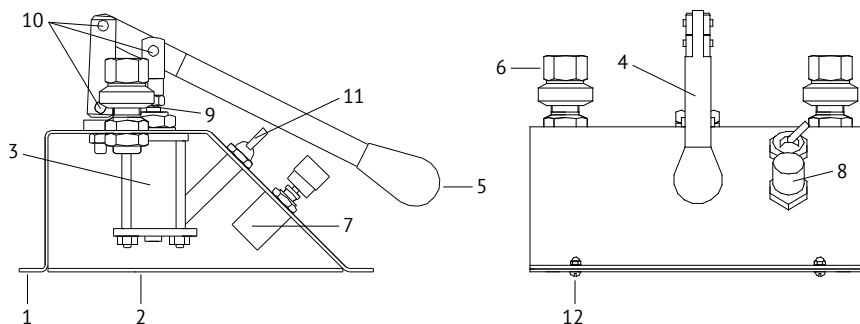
Пневматическое устройство для сравнительной калибровки:
